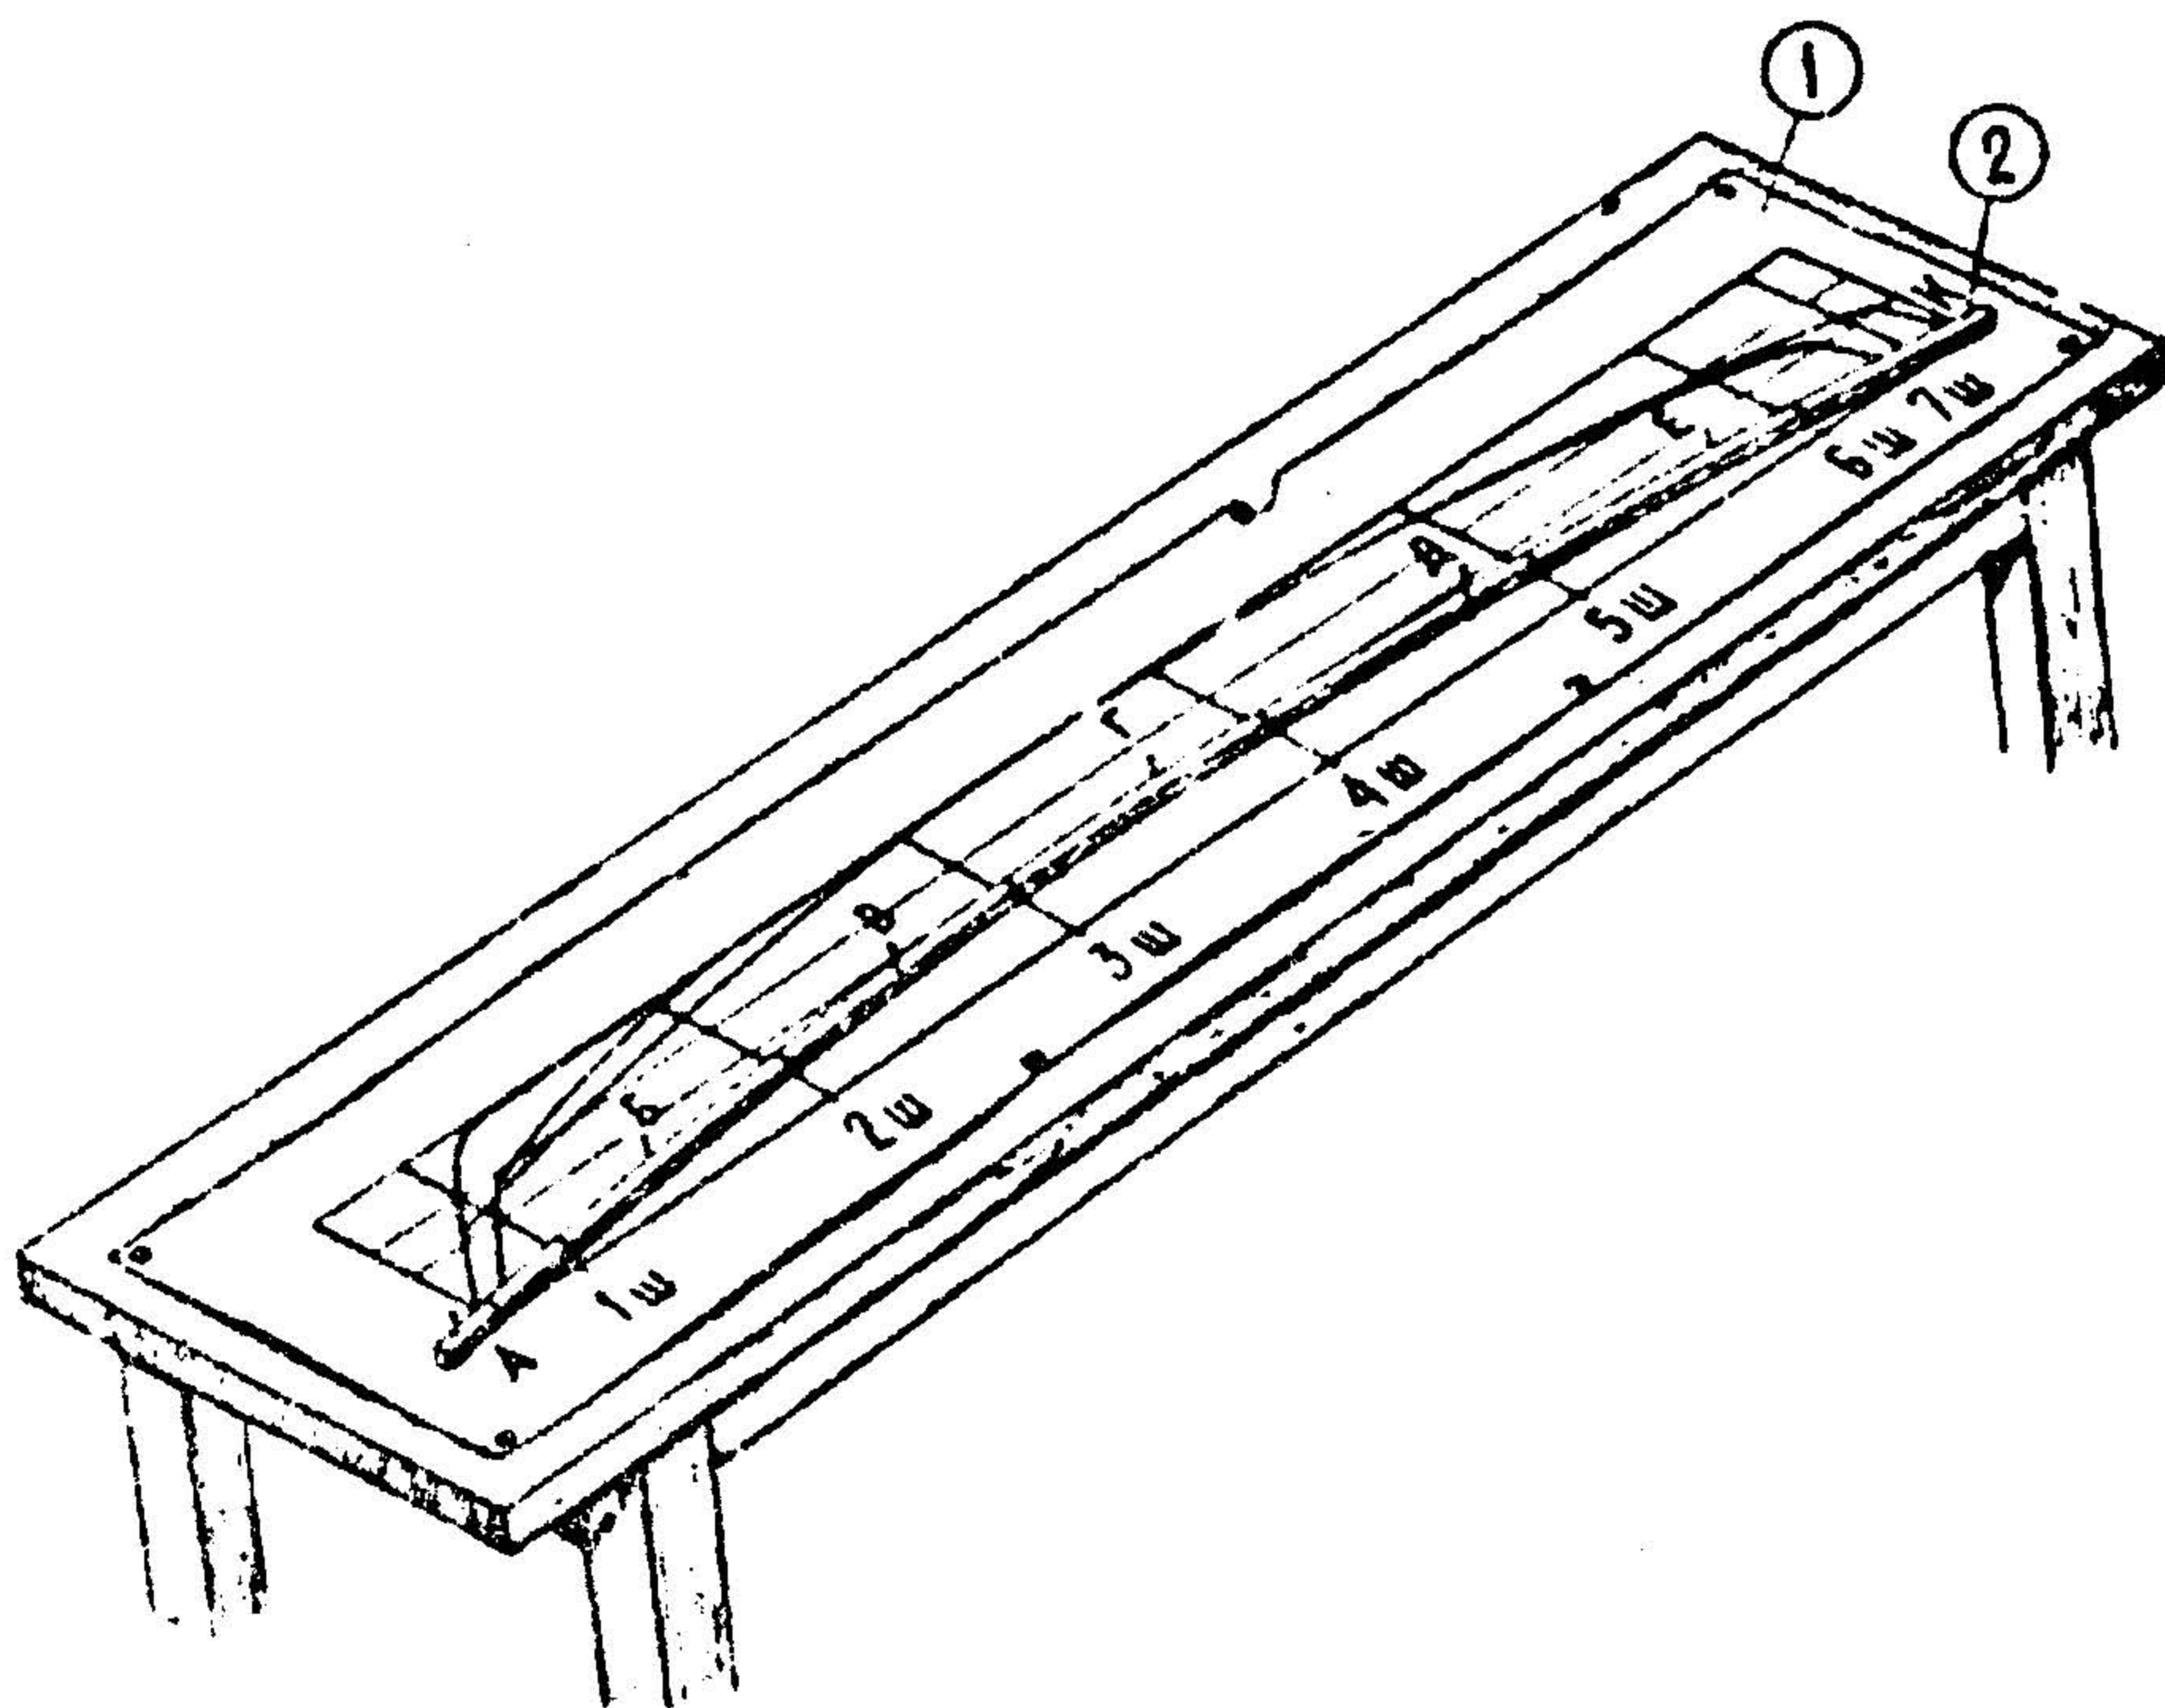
Разметка плавовой рейки: 1 — теоретический чертеж; 2 — плавовая рейка
